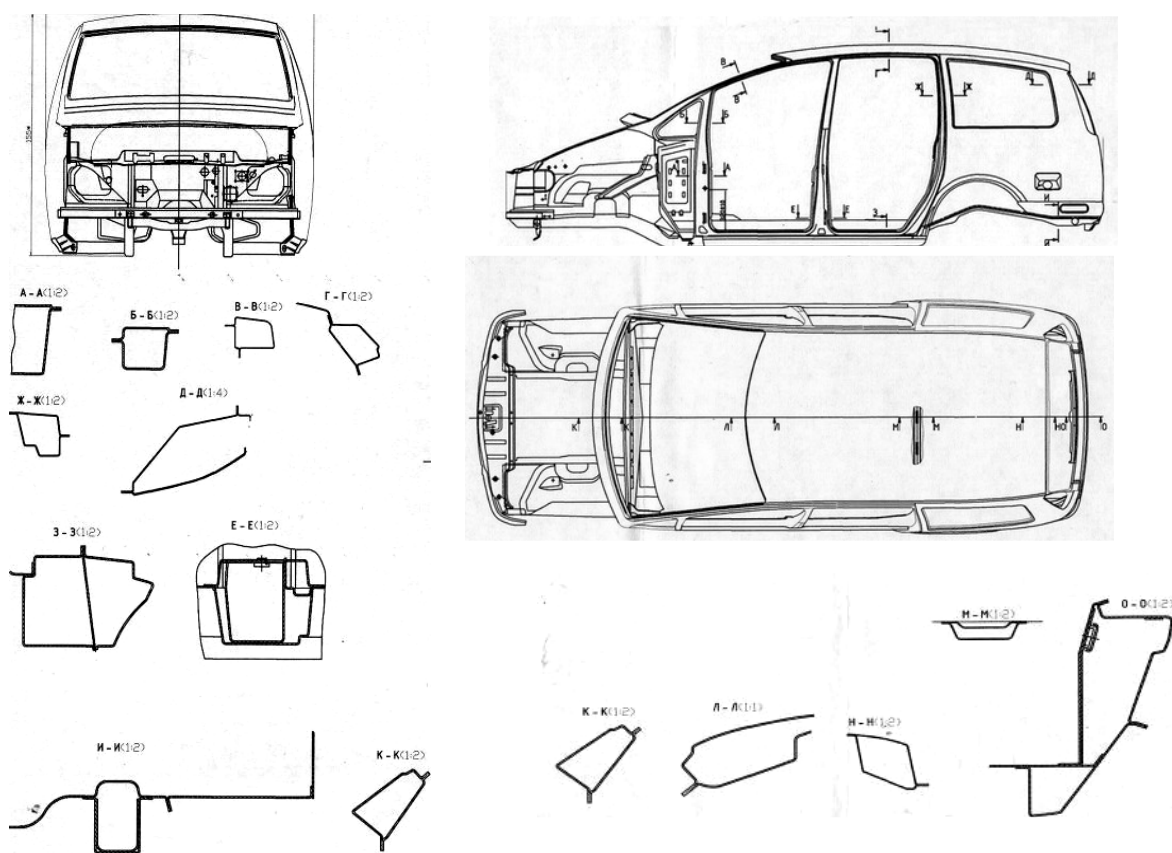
Конструктивные чертежи кузова легкового автомобиля
